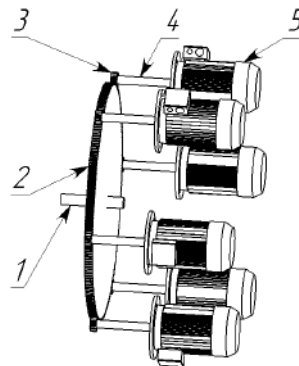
Конструктивна схема одноступеневого редуктора з кількома вихідними валами.
